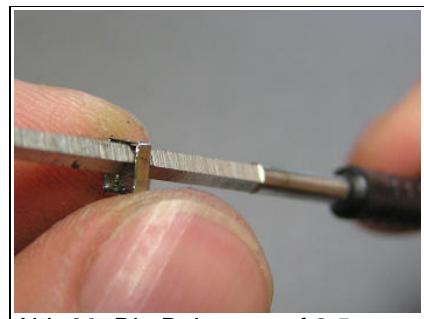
Die Bohrung auf 2,5mm aufreisen oder bohren. (Bunddurchmesser des 1:5 Getriebemotors). Siehe Abb. 22
